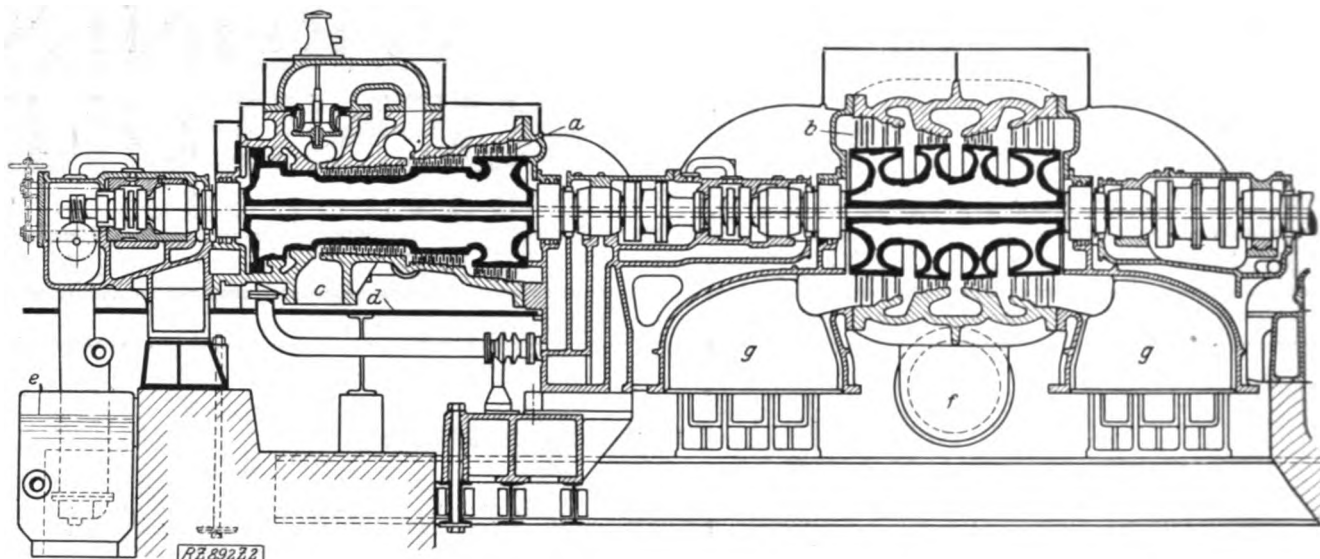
C. A. Parsons & Co., Ltd., Zweigehäuse-Zwillings-Überdruckturbine, 12 000 kW, 3000 Uml./min.
